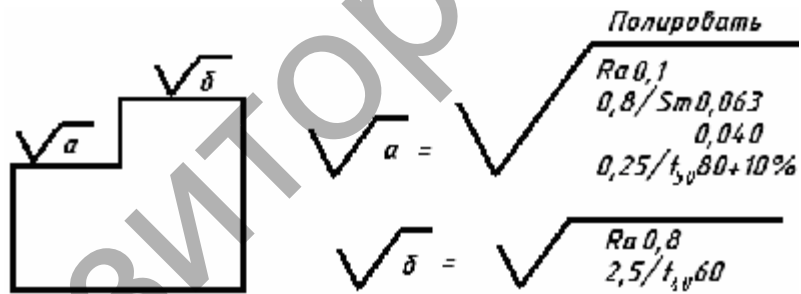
Примеры обозначения шероховатости поверхности
